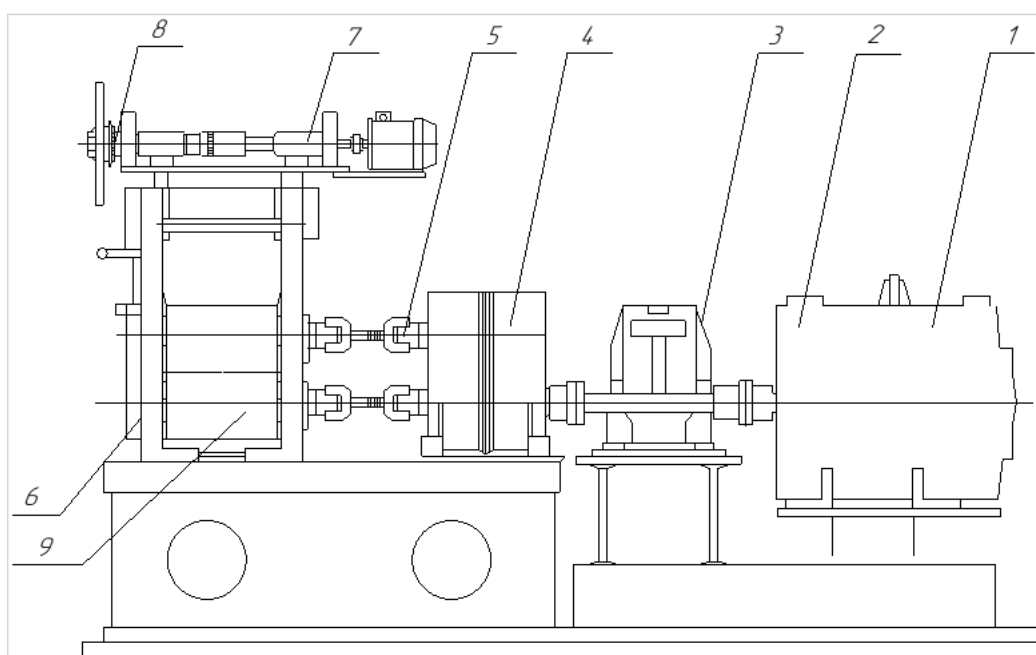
Общий вид рабочей линии клетки ДУО-180
